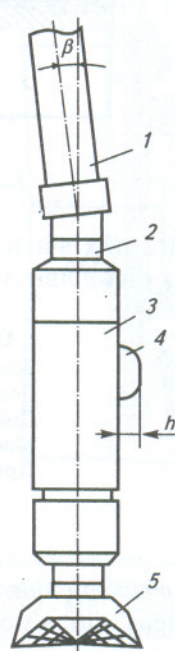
Схема відхилювача з накладкою: 1—бурильні труби; 2—кривий перехідник; 3—турбобур; 4—накладка; 5—долото; (h —товщина накладки; β —кут перекоосу приєднувальної різьби)
